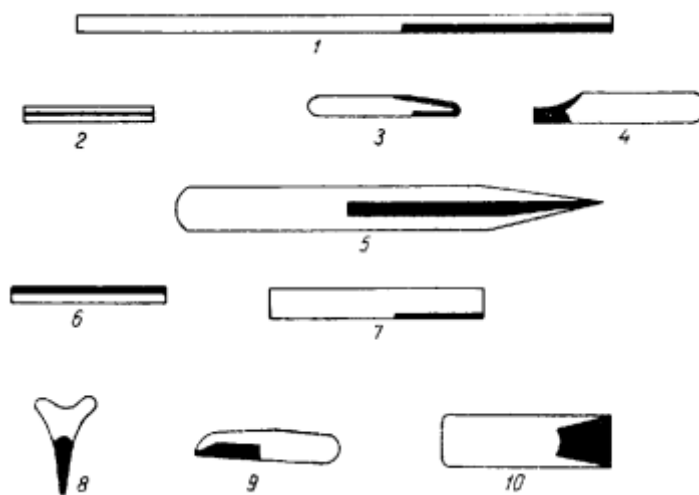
Види біметалічних профілей для використання, як ріжучий інструмент та для інших цілей: 1 – залізяка для рубанка скошена; 2 – ніж для шкіри; 3 і 4 – ножі для газонокосарки; 5 – обдирний ніж; 6 – зубчаста смуга і жниварка; 7 – ніж для різки паперу і шпону; 8 – спіраль для різки тканин; 9 – ніж для газонокосарки; 10 – коса.
